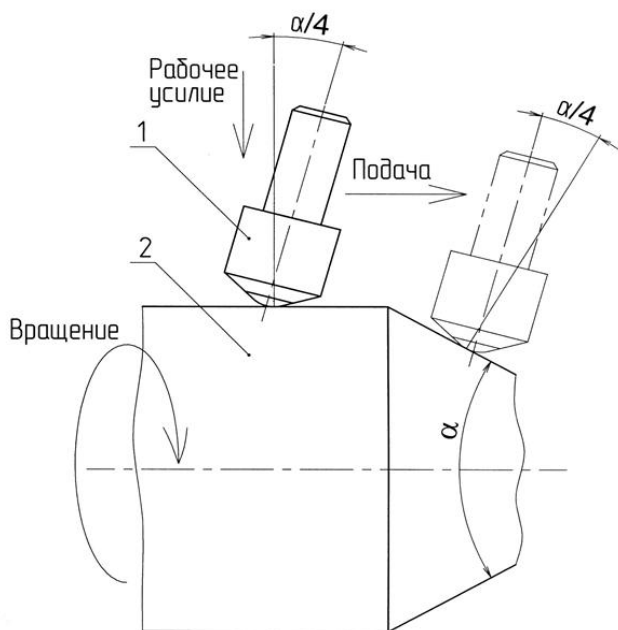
Положение оси инструмента относительно обрабатываемой поверхности детали в процессе обработки
